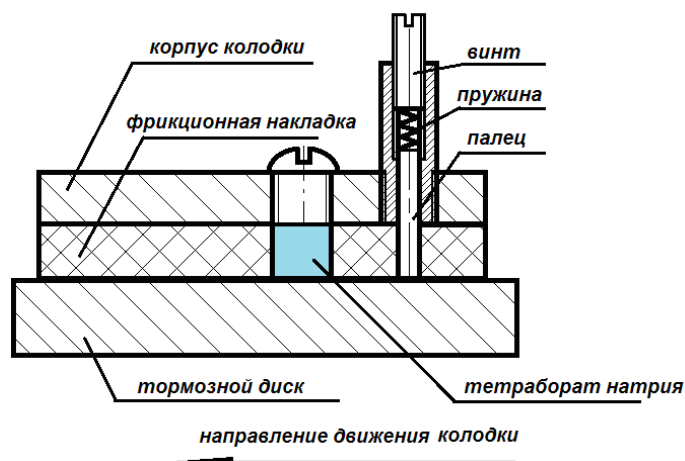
Схема установки для испытаний с активатором поверхности
